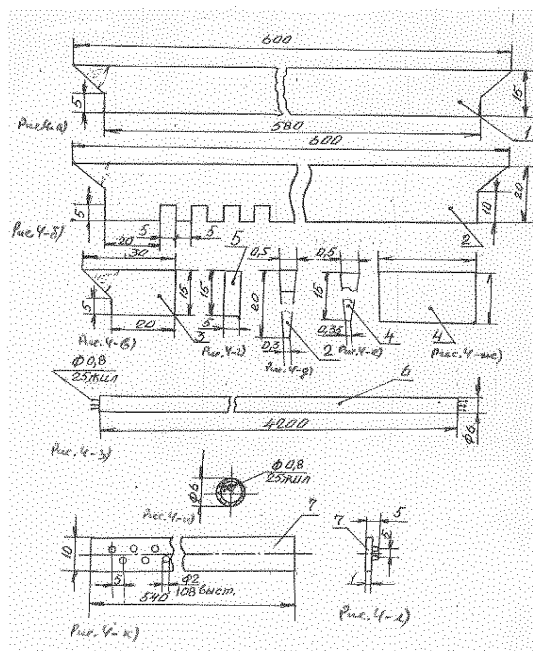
Комплектующие детали индуктора и обмотки (Рис.4 по источнику /3/)
